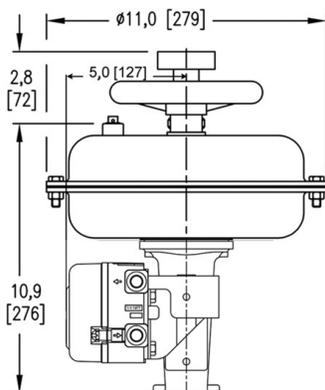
РАЗМЕРЫ - дюймы [миллиметры]
